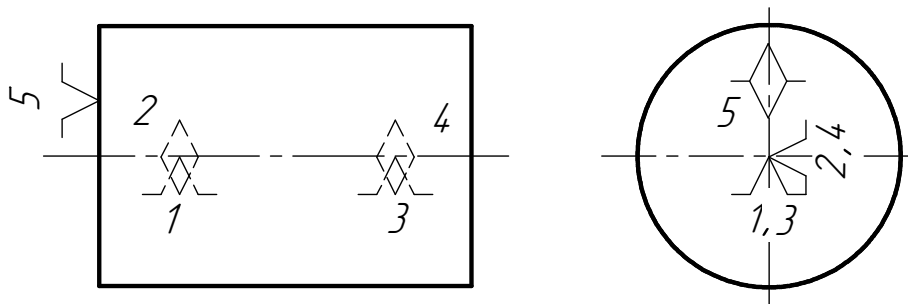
Теоретическая схема базирования при установке цилиндрического валика по оси заготовки
